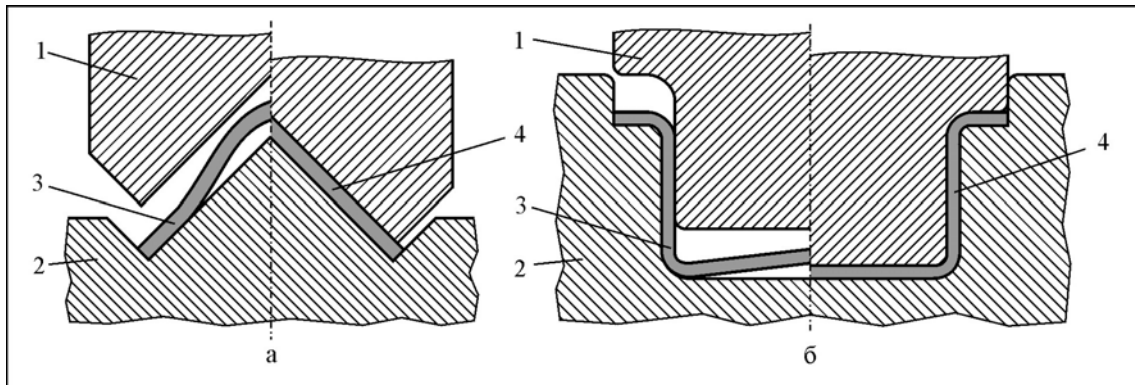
Правлення заготовок з калібруванням полиць: а – після однокутового гнуття; б – після чотирьохкутового гнуття; 1 – пуансон; 2 – матриця; 3 – заготовка; 4 – виріб
